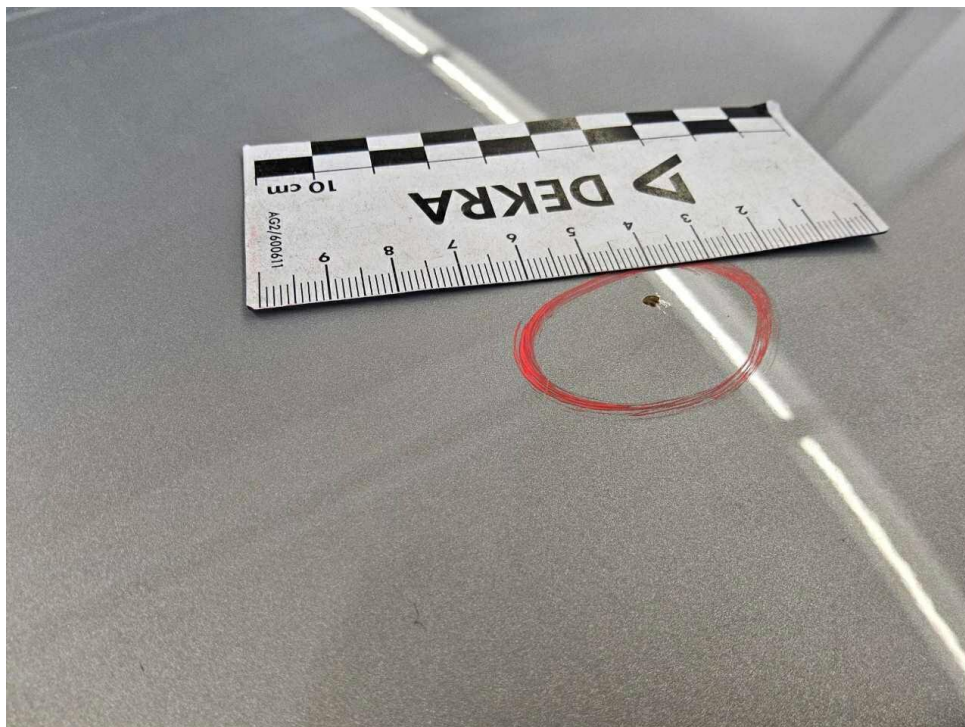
Dach, korrodiert, lackieren mit Lackaufbau
